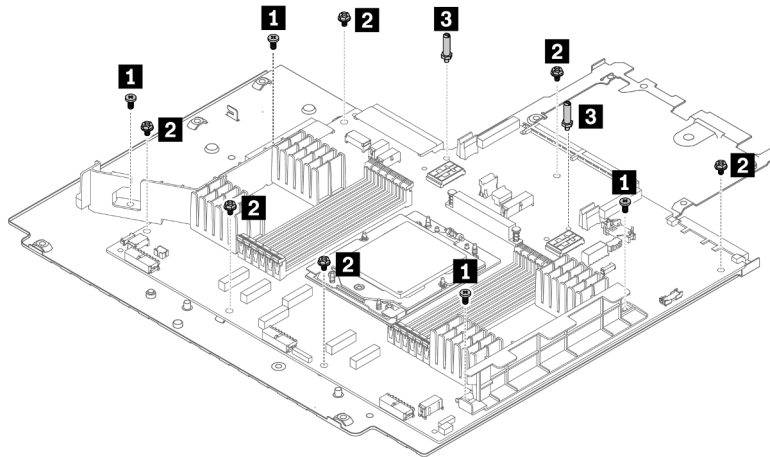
Entfernen der Schrauben von der Prozessorplatine
